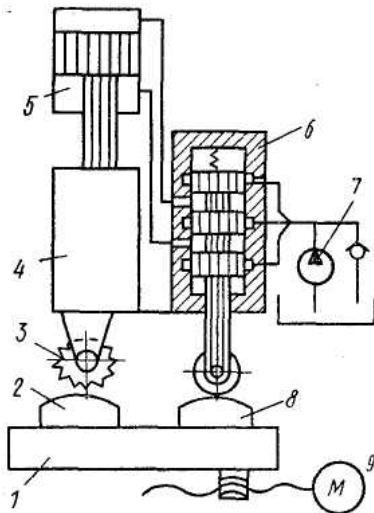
Принципиальная схема гидравлического следящего привода фрезерного станка:
